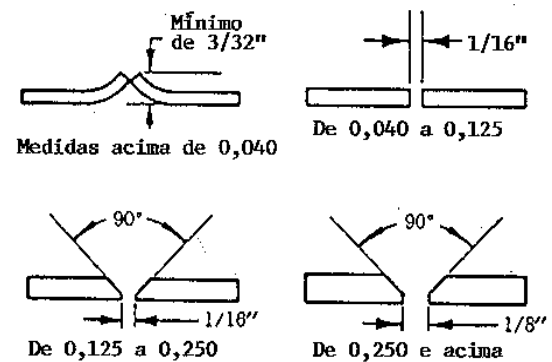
Preparação das bordas para a soldagem de chapas de magnésio.
